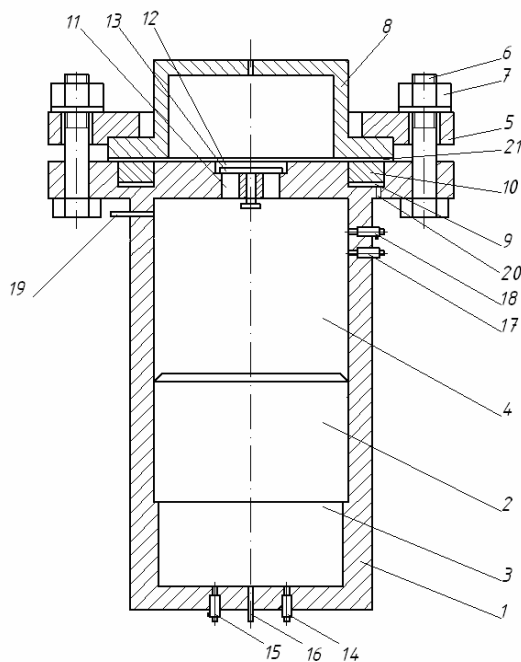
Схема двухкамерного устройства газовой штамповки:
